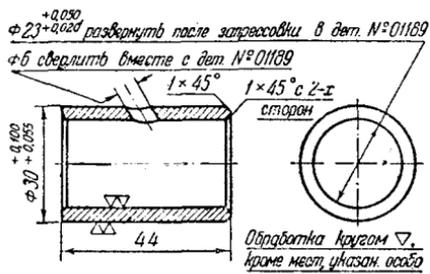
Дет. № 01195. Втулка в корпус распределительных шестерён
